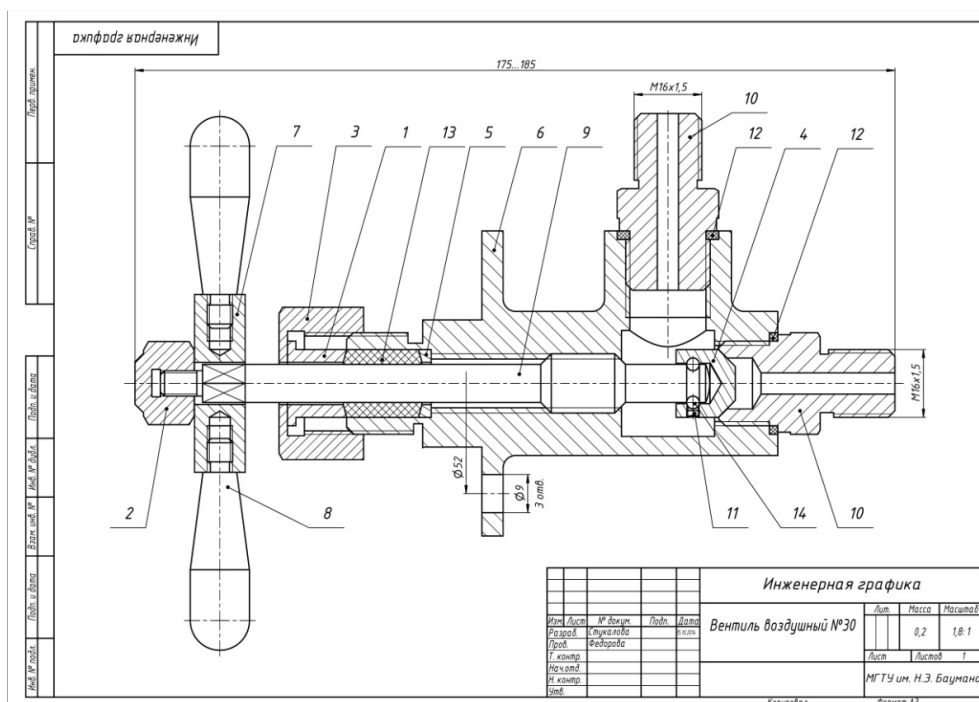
Сборочный чертеж «Вентиль воздушный №30»
